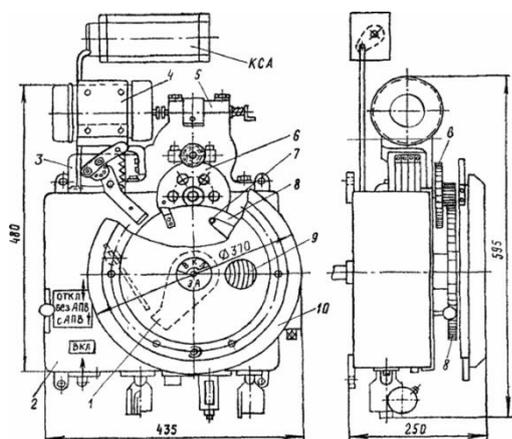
Пружинный привод с моторным редуктором ППМ-10:
